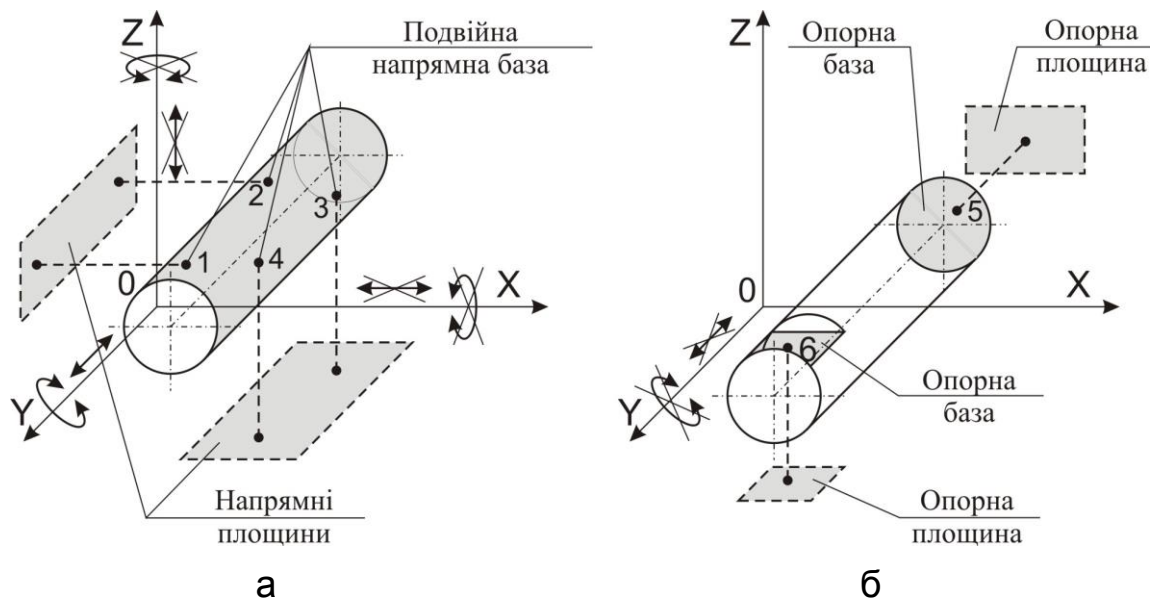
Комплект баз циліндричної заготовки:
